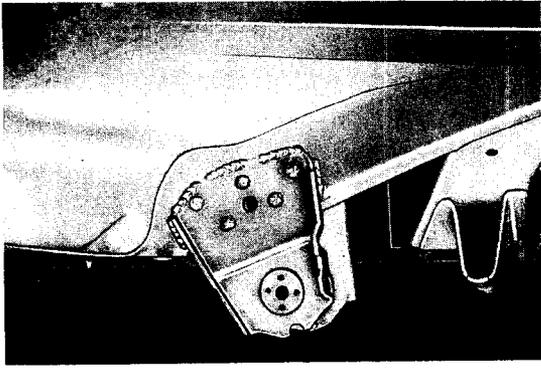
Hinterfederstützen an Steg des Hinterlängsträgers lichtbogengeschweißt
